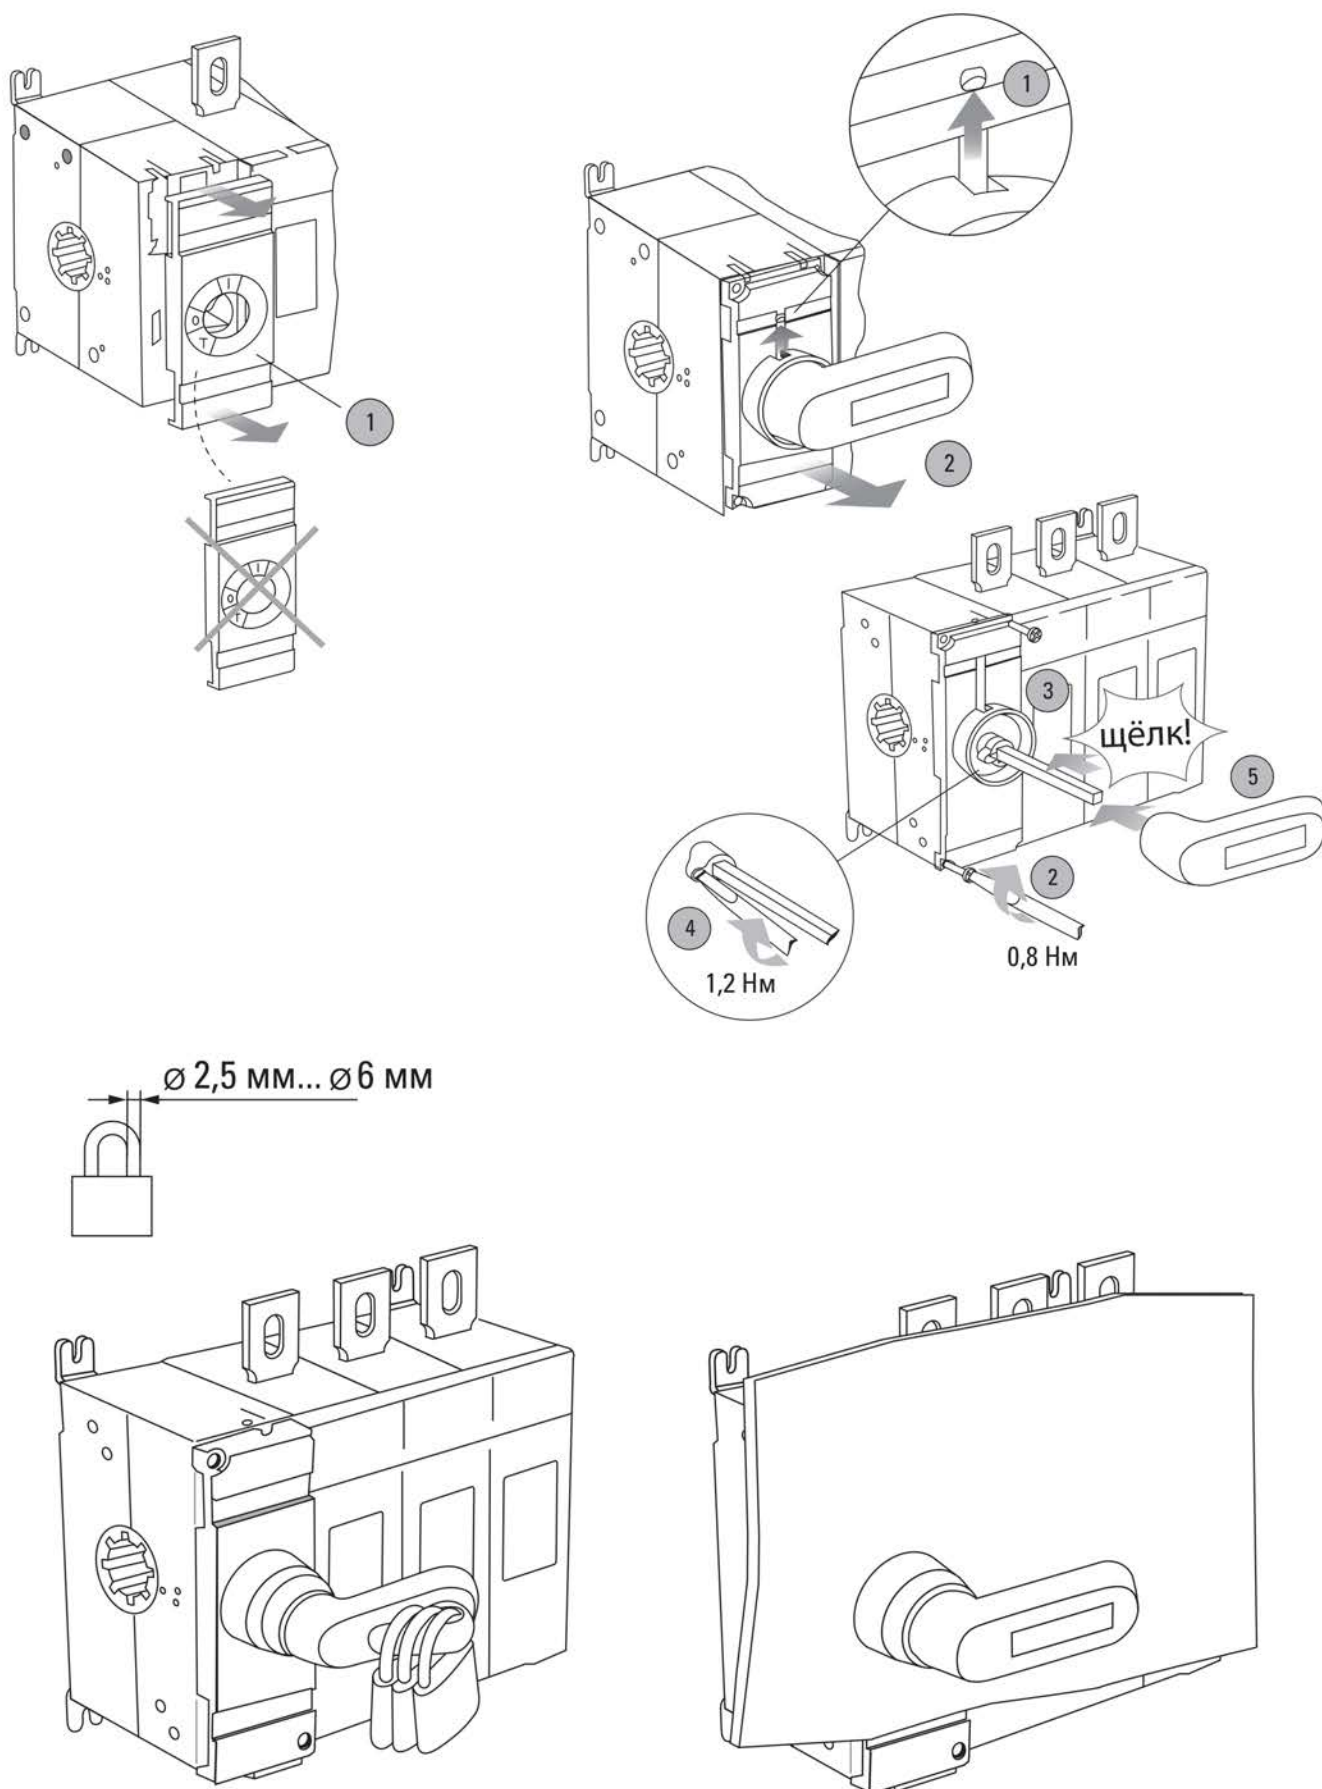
Установка рукоятки управления прямой установки 315-1600А
